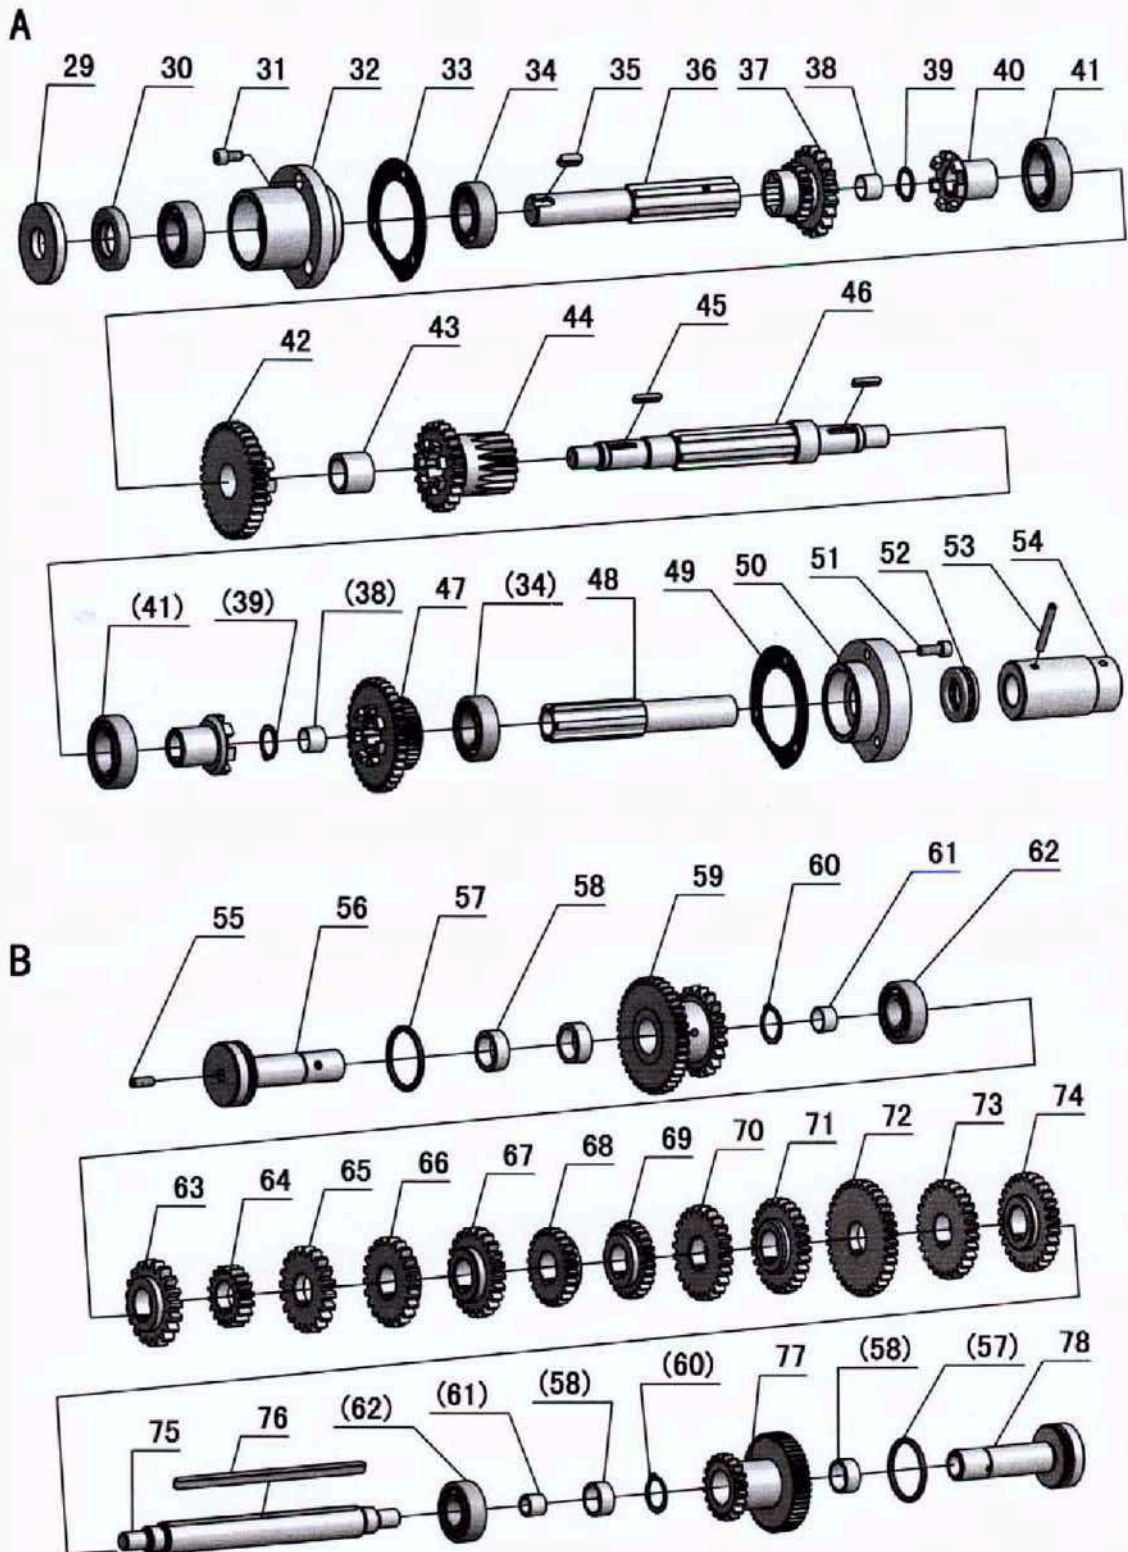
Vorschubgetriebe 2 von 4 - Headstock feed gear 2 of 4
